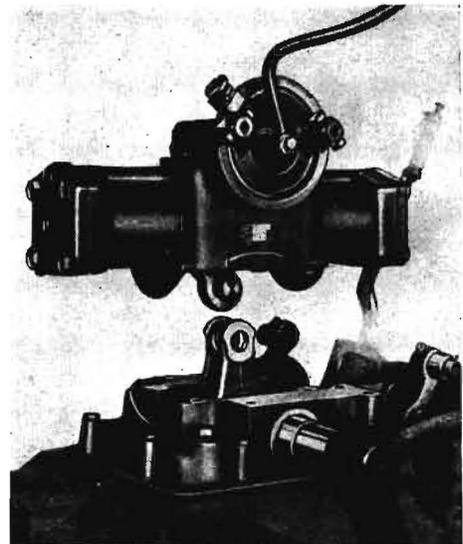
Hydraulischer Kraftheber (Regelzylinder) von Teves
